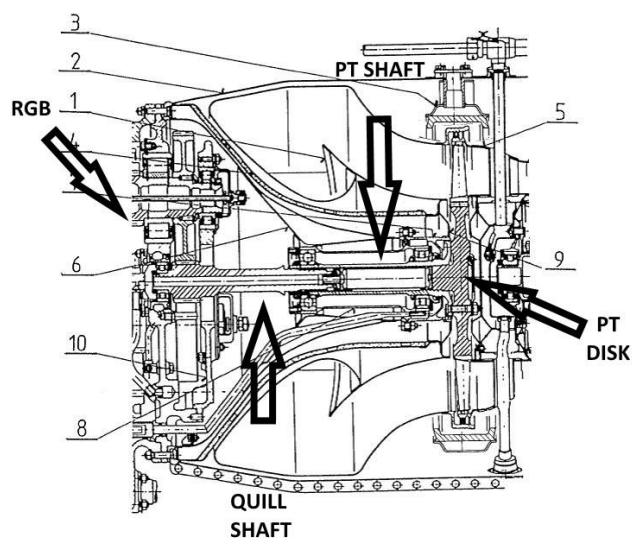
PT shaft* e *quill shaft* all'interno del *supporting cone*, tra *power turbine* e *reduction gearbox*.
